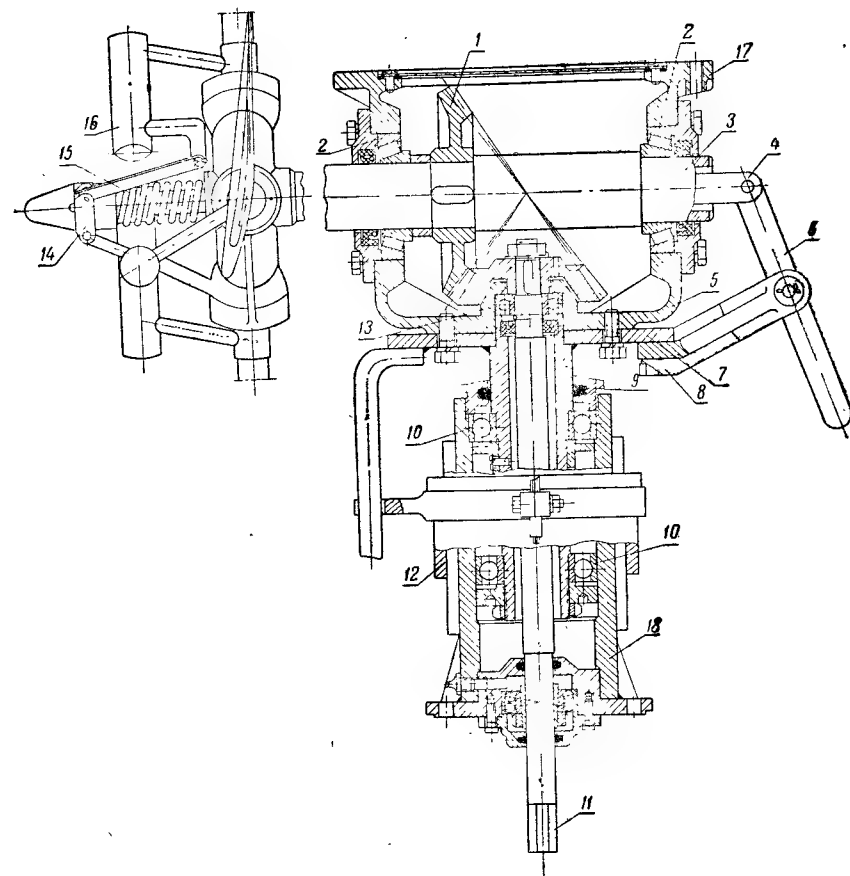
Головка ветроустановки ВВУ-3 с регулятором:
